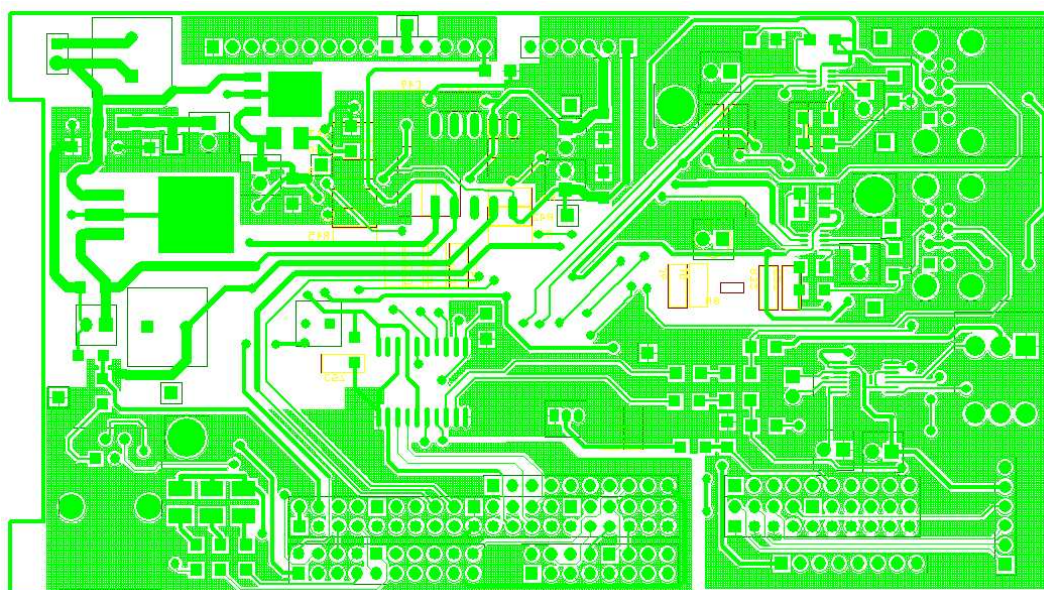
Layout do PCB da LocusBoard - Top (Fonte: [17]).
